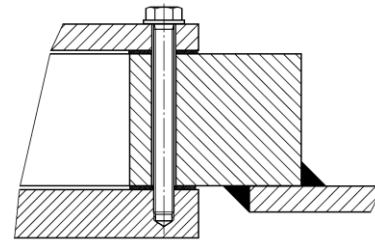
Disposiciones de montaje con cabezal, cubierta plana y pernos estándar.
